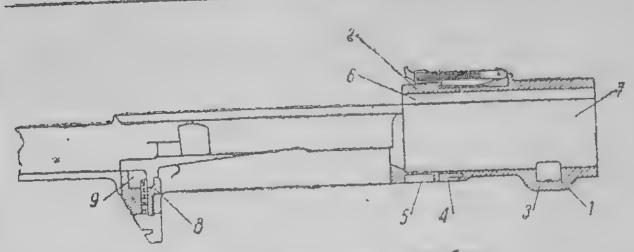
Ствольная коробка: 1-клин; 2-основание прицела; 3-прилив для клина; 4-гнезда для выступа магазина; 5-гнезда для выступа пружины рычага подавателя; 6-канал для толкателя затвора; 7-канал для помещения казенной части ствола; 8-паз для останова затвора; 9-вкладыш
